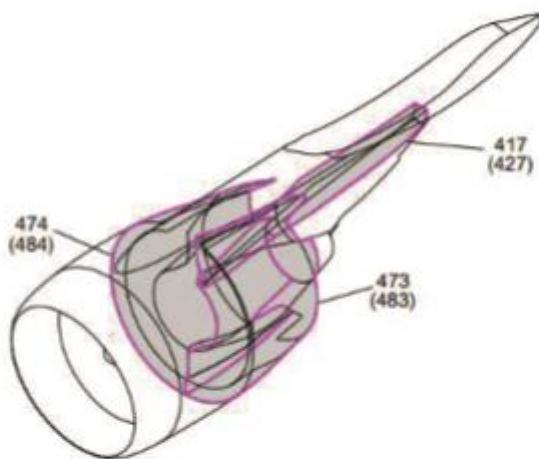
Расположение датчиков пожара-перегрева на двигателе
